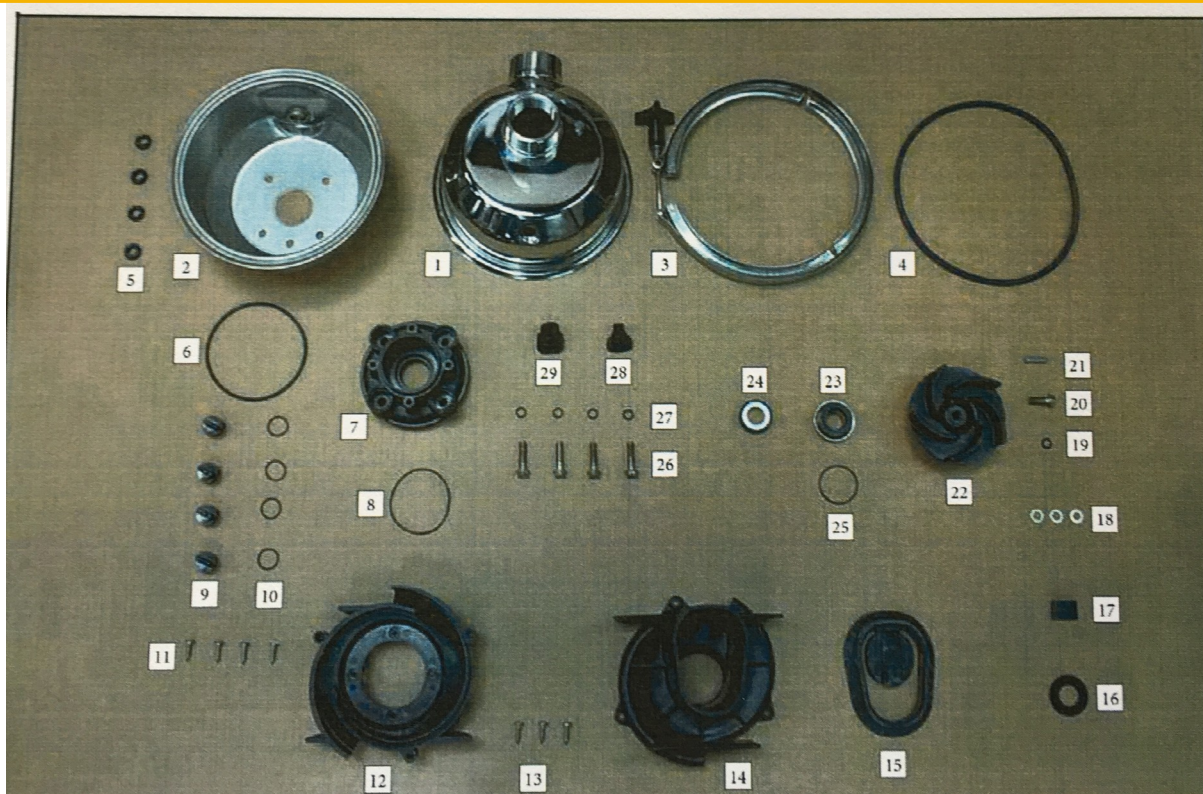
Despiece de la bomba INOX 50, en acero inoxidable AISI 316
